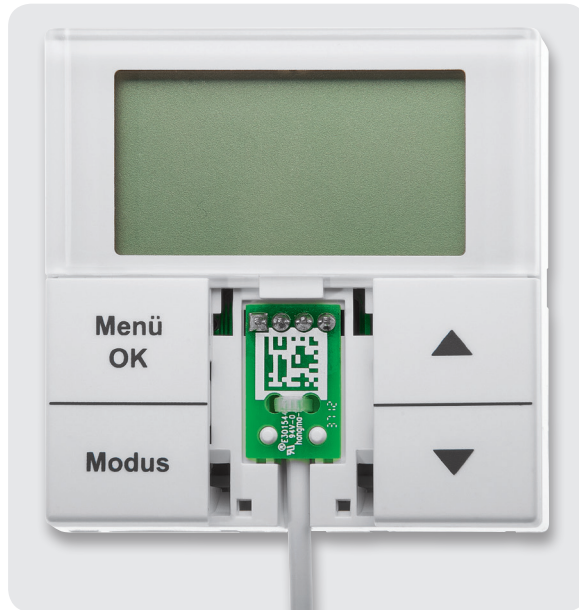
Jetzt wird die Steckerplatine eingesetzt und abschließend die Gehäuseabdeckung wieder aufgesetzt.
